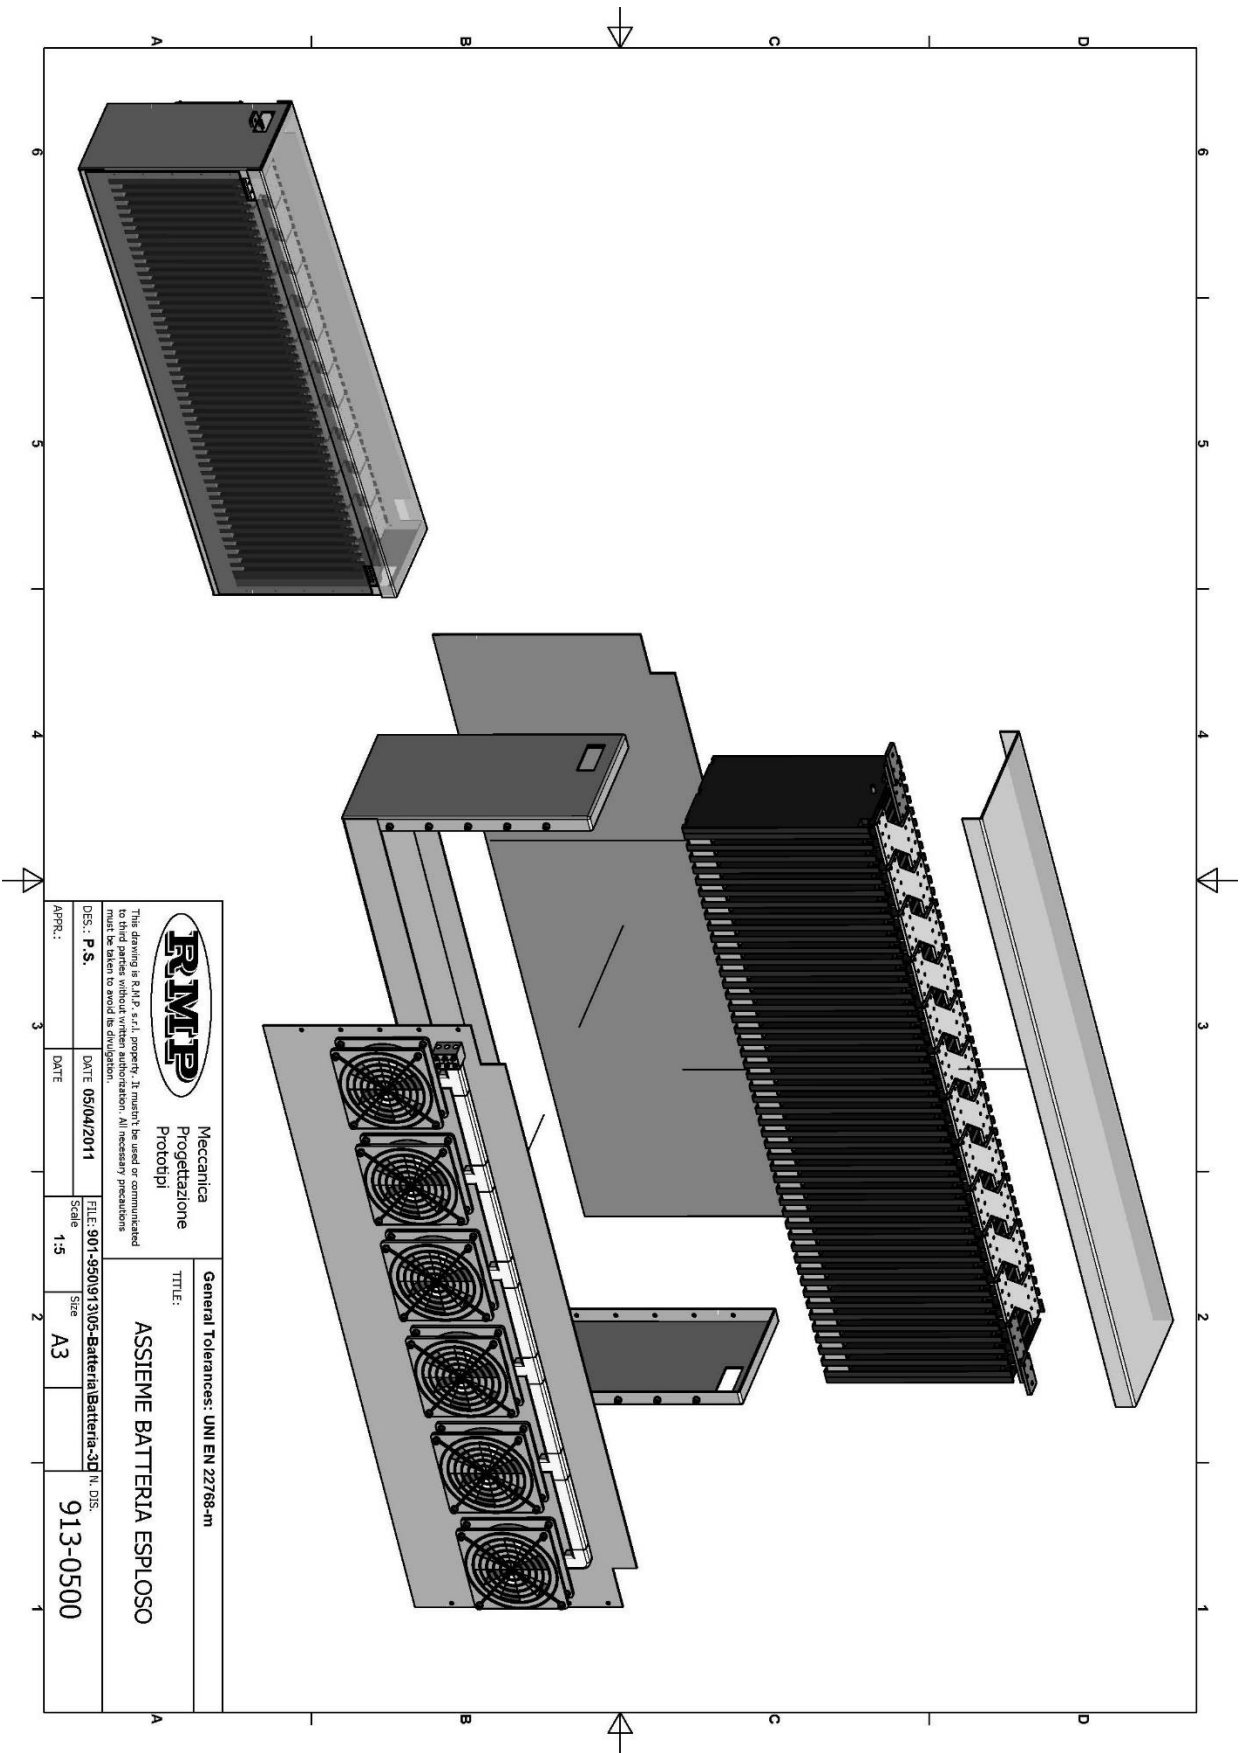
Disegni di assemblaggio del modulo di Bergamo – parte esterna
